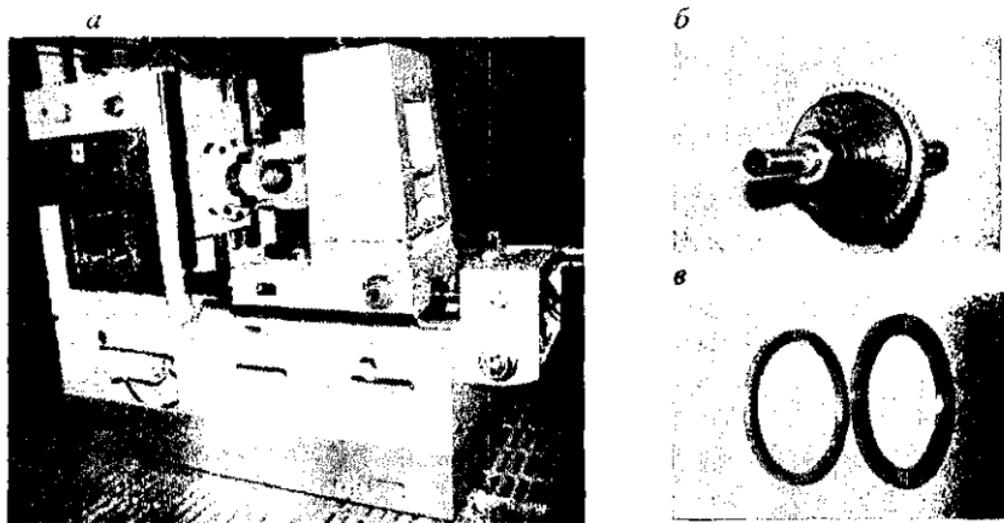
Станок модели BC-30II-9253 для обработки индукторов АБС автомобилей:
